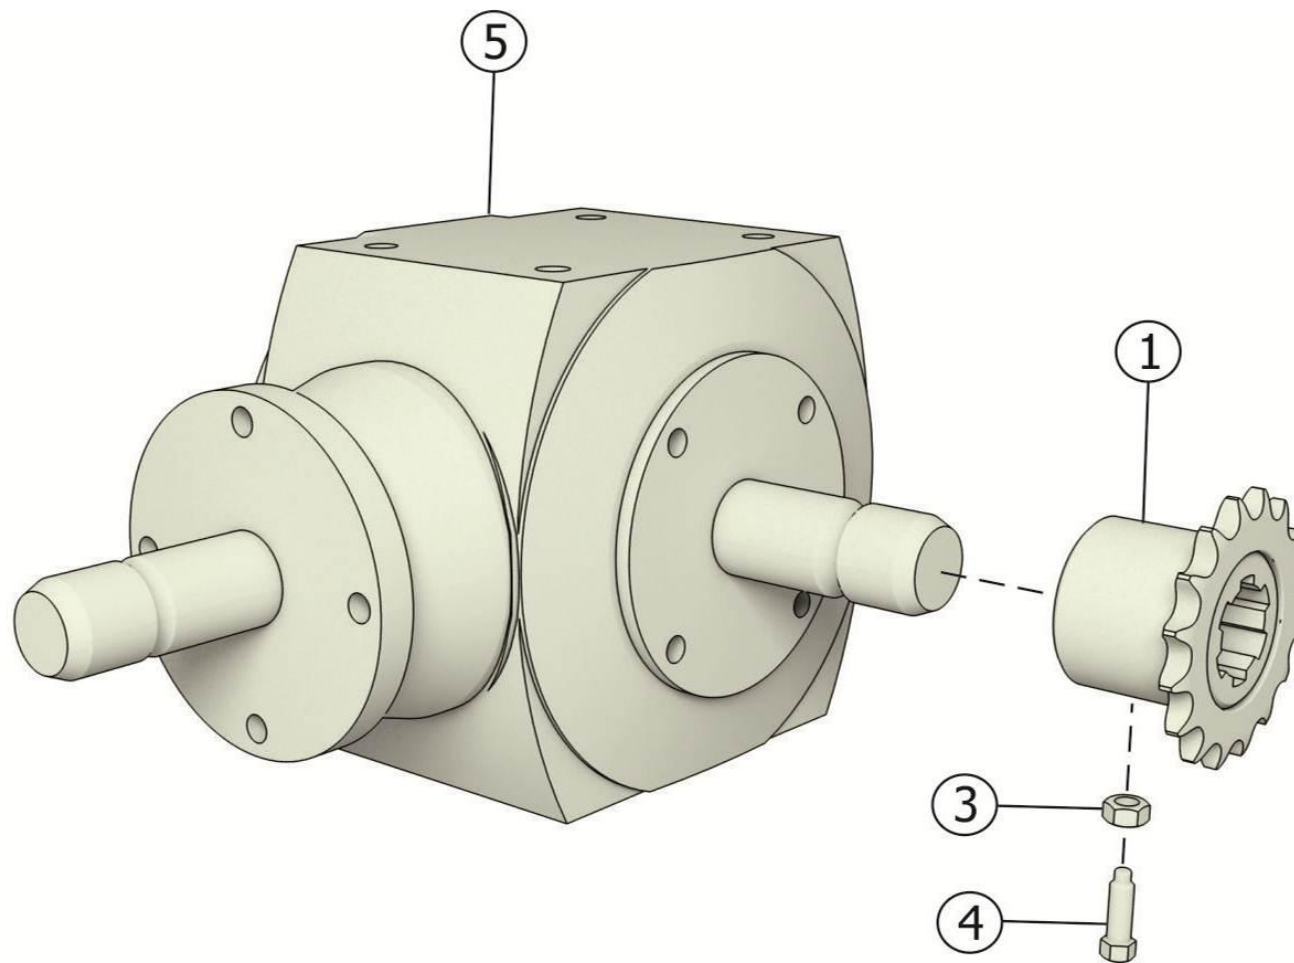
Редуктор ПСП-10МВ.01.01.590А-01
